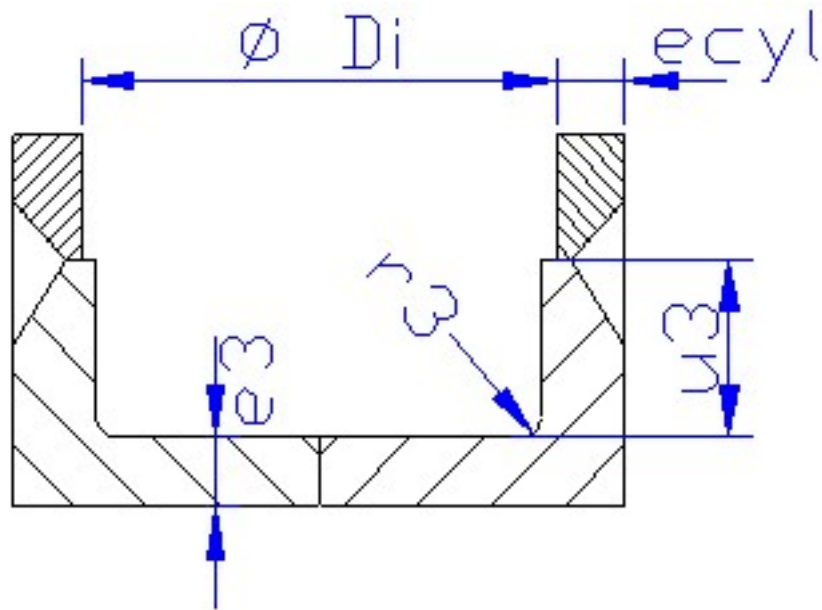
Esquema de fondos planos con bridas soldadas.
